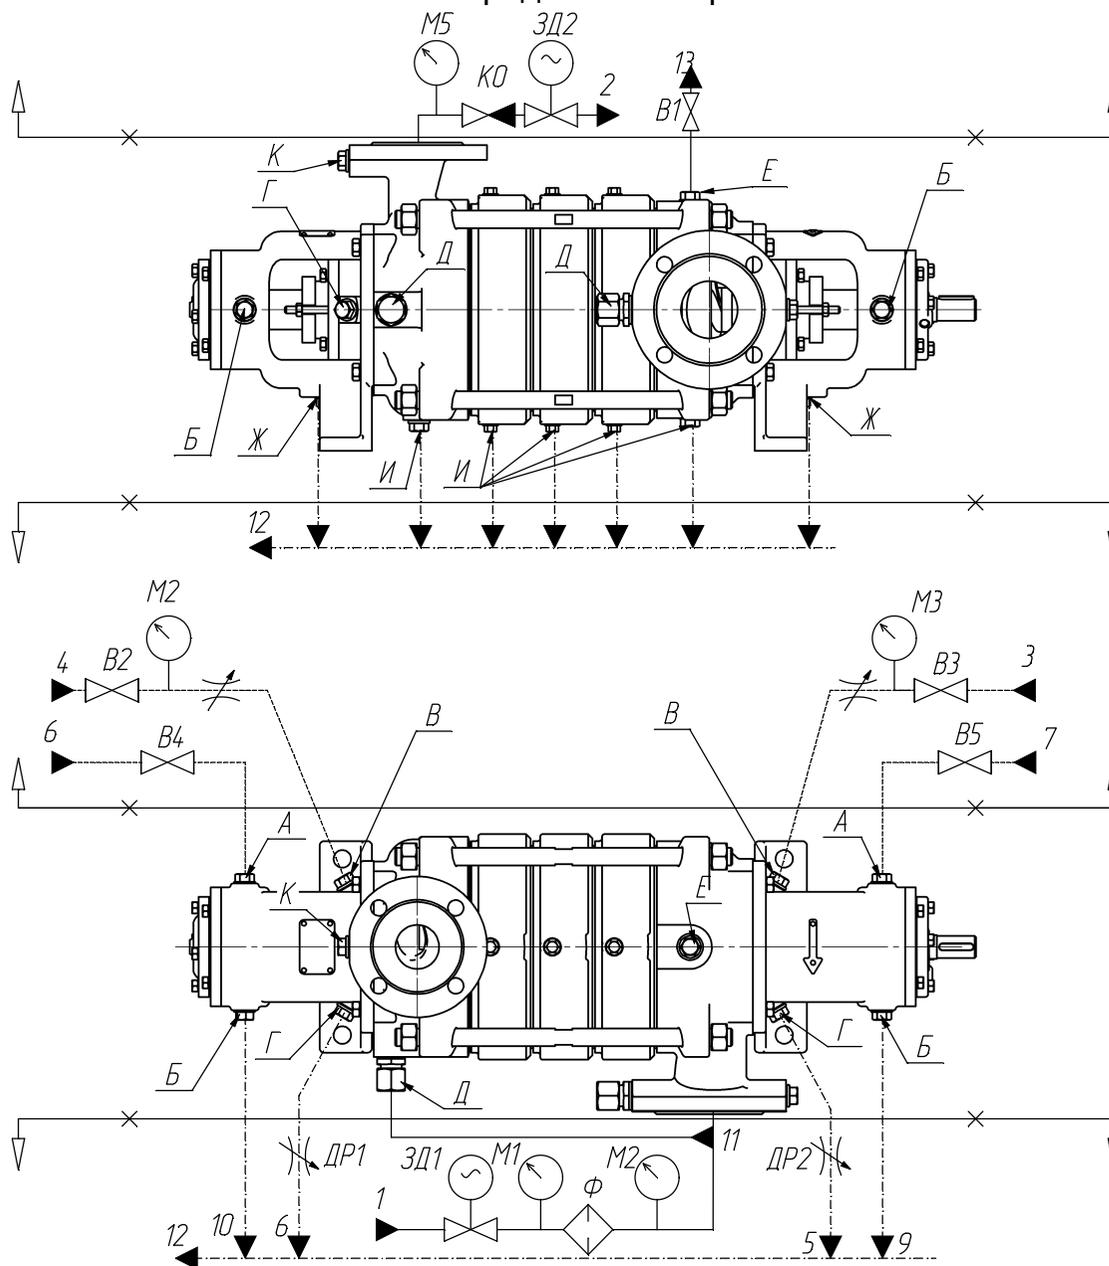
Схема подключения вспомогательных трубопроводов насосов 1Кс12, 1Кс20
